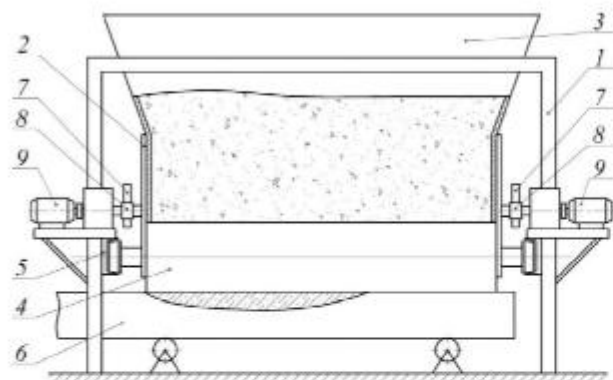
Роликова формувальна установка з кулачковим приводним механізмом
